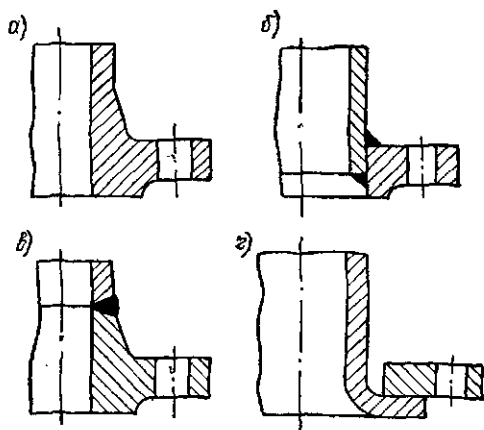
Различные конструкции фланцев: а — литые кованные; б — приварные; в — приварные с шейкой; г — свободные на отбортовке.
